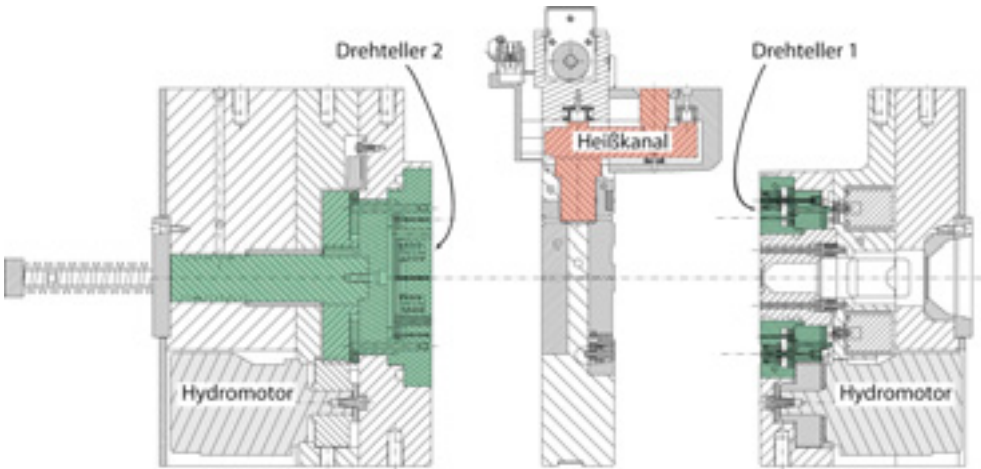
Overmolding Tandemwerkzeug mit 2 integrierten Drehtellern [13.17, 13.21]
